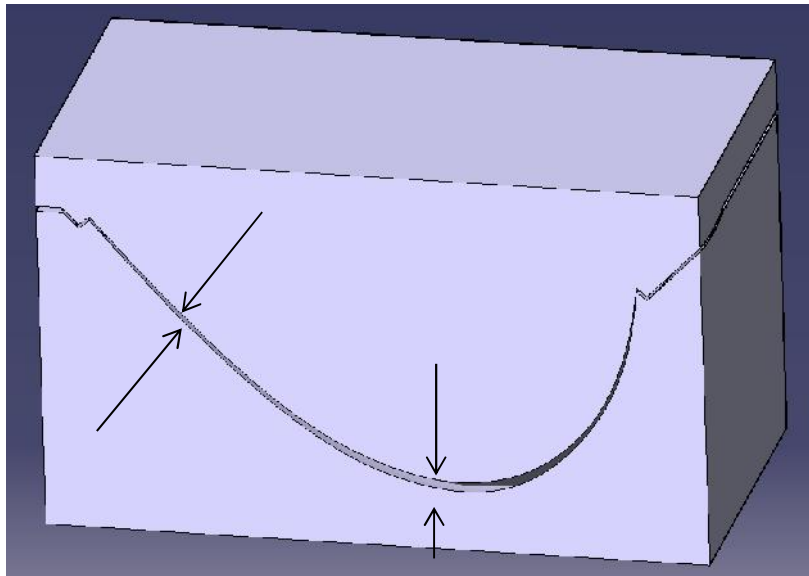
Unión (referencia a espesores) de molde macho y molde hembra
